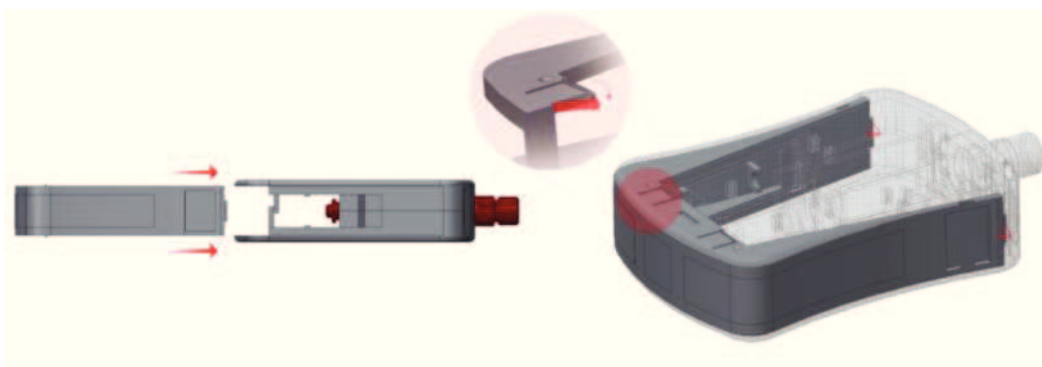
Componente de moldura e o seu formato de encaixe ao corpo principal.
